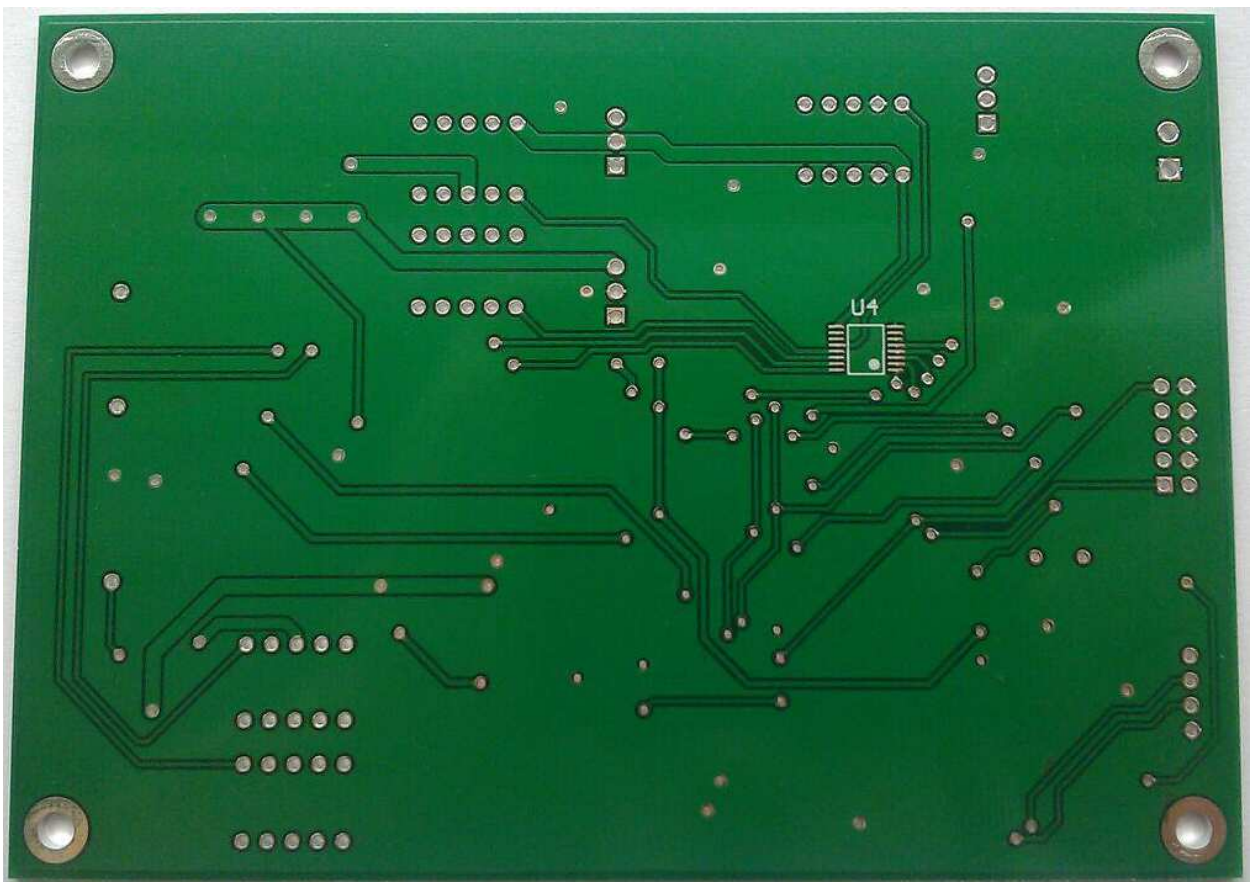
Виготовлена друкована плата пристрою (вид знизу)
